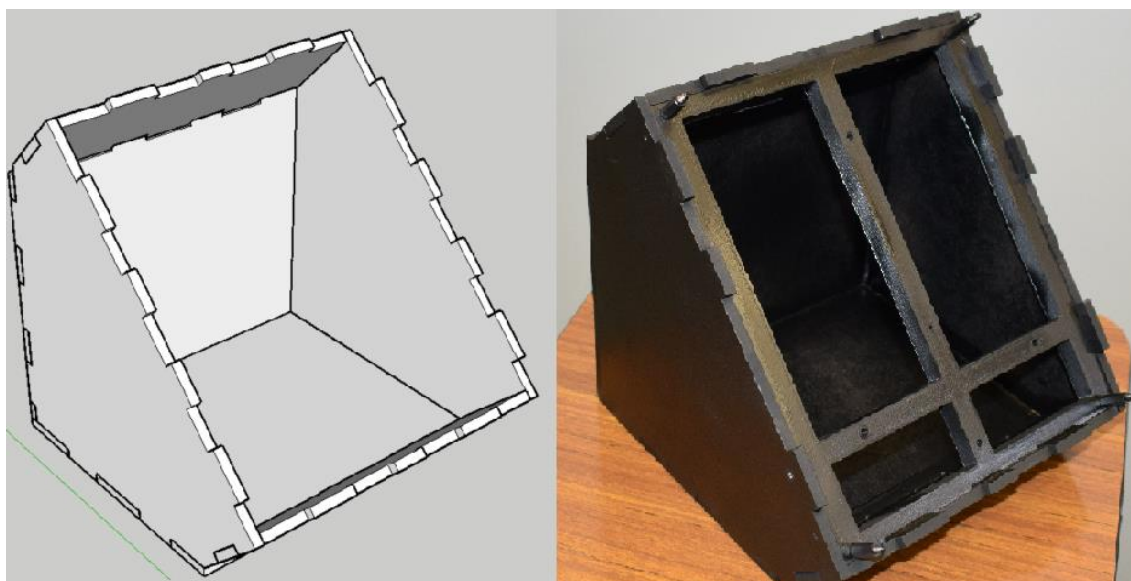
Caja y soporte del PCB. Diseño y resultado final
